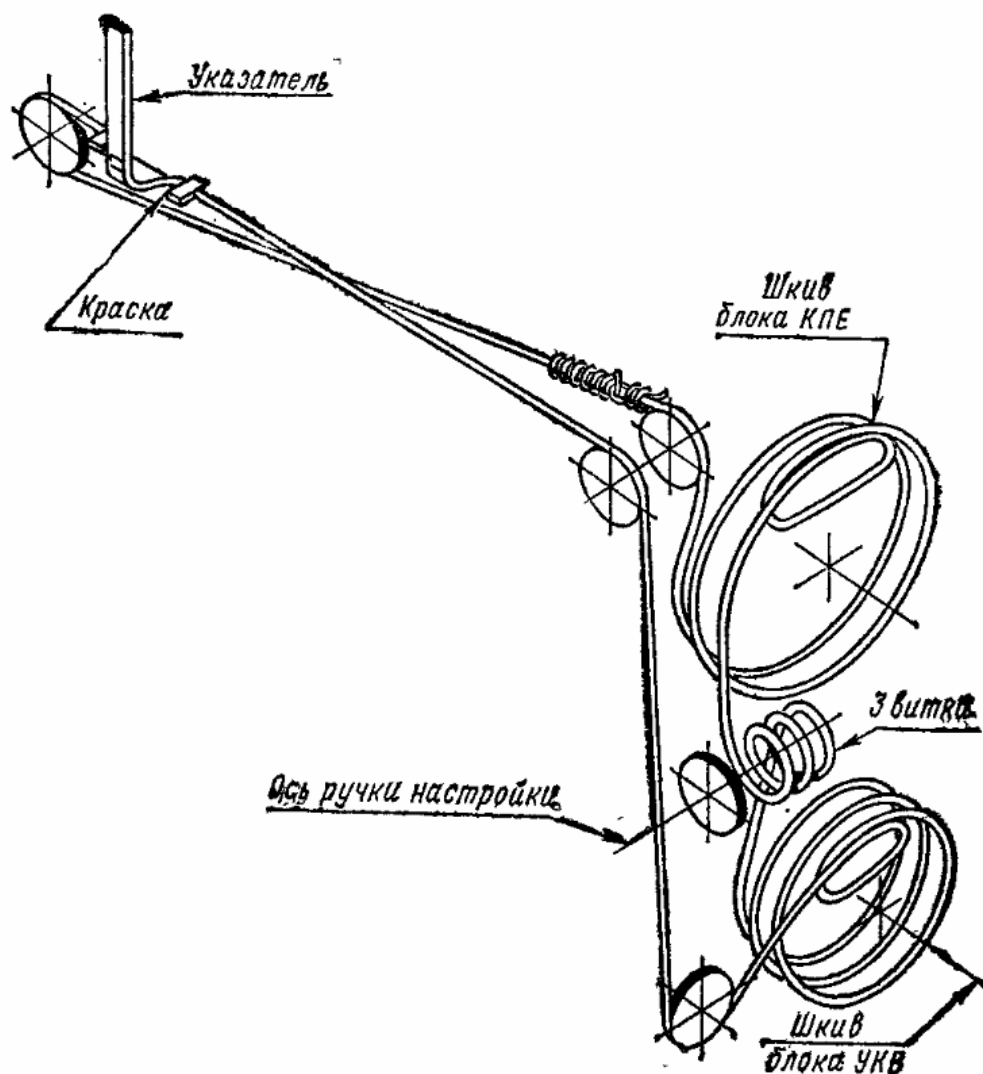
Кинематическая схема верньерного устройства приемника «Океан-205».
